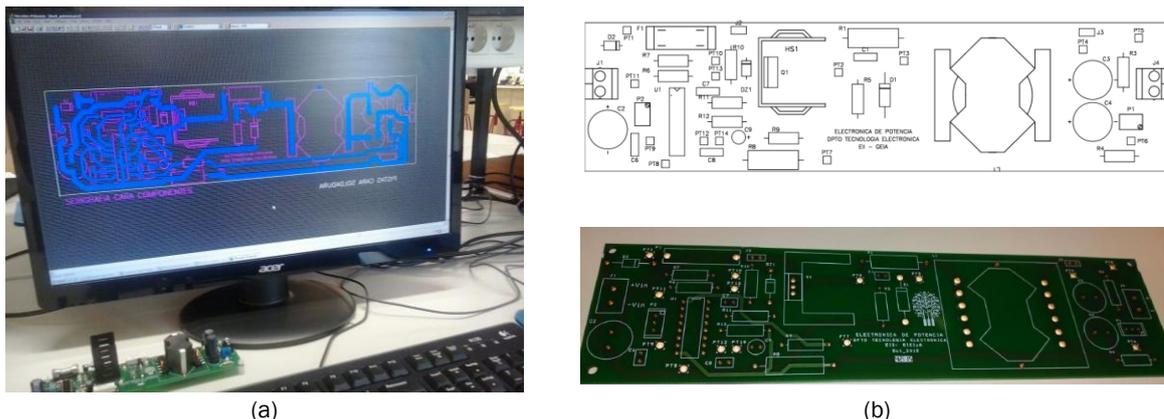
Diseño del PCB empleado en el prototipo del BUCK: (a) Rutado de la tarjeta; (b) Serigrafía y tarjeta PCB.
